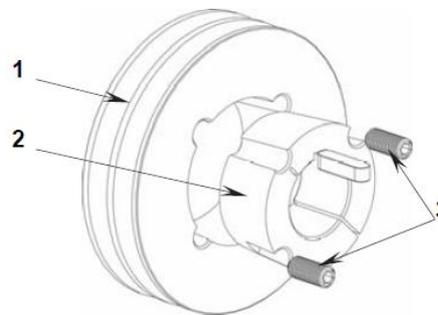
Шкив ременной передачи и втулка типа "Tape-Lock"
